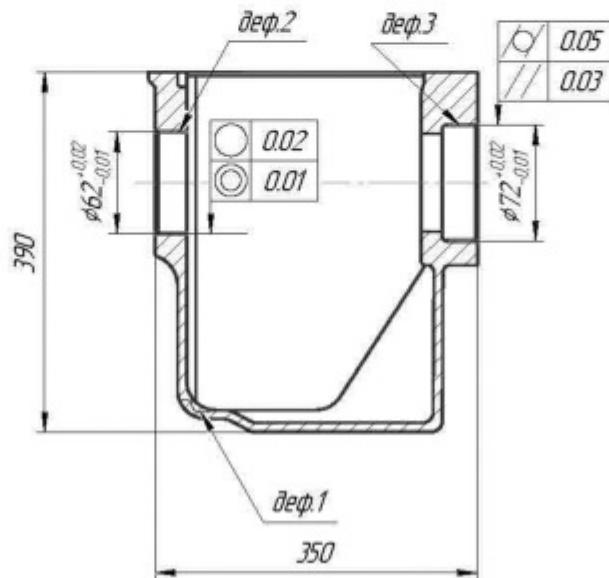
Схема измерения отверстия под подшипник.
